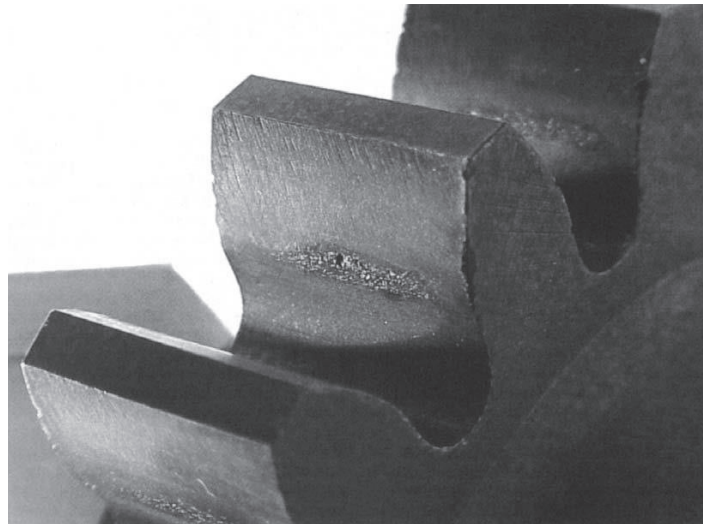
Engranaje recto con micropitting cerca de la línea de paso
